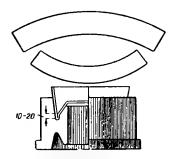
Прессформа и заготовка для :миканитового коиуса.
